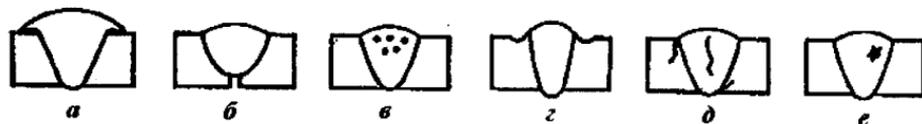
Види дефектів зварних з'єднань: а - наплив; б – непровар; в – пори; г – підрізи; д – тріщини; е – вкраплення.
